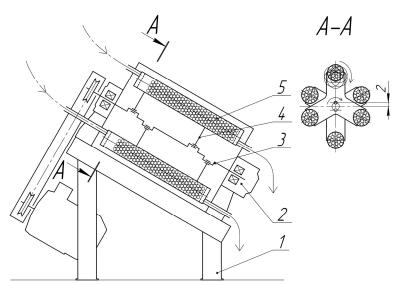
Кинематическая схема вибропланетарной мельницы «Пурга»: 1 — рама, 2 — подшипниковые опоры, 3 — эксцентриковый вал, 4 — водила, 5 — барабан
